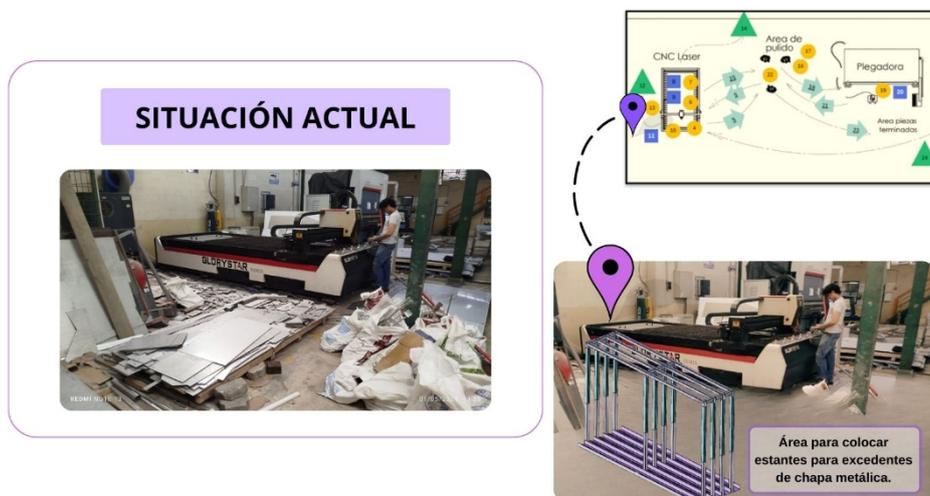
Opción 3: Diseño y plano de estantería para sobrante
